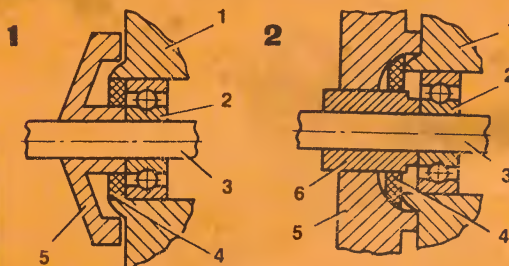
Узел переднего колеса: 1 — ступица; 2 — левый подшипник; 3 — ось; 4 — кольцо-сальник; 5 — защитный колпачок.
